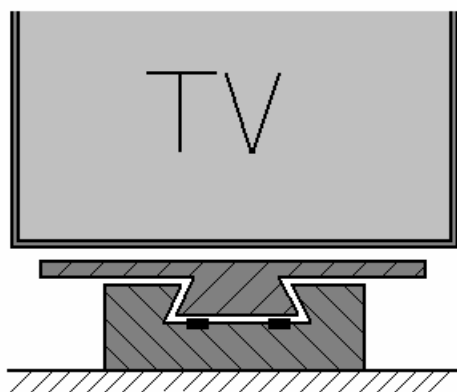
Varianta I. – způsob naklápění televizoru
